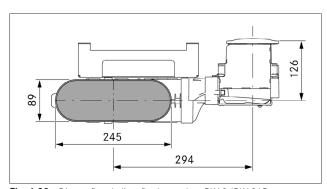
Dimensões da ligação de conduta PKA3/PKA3AB com peça da conduta em cotovelo
